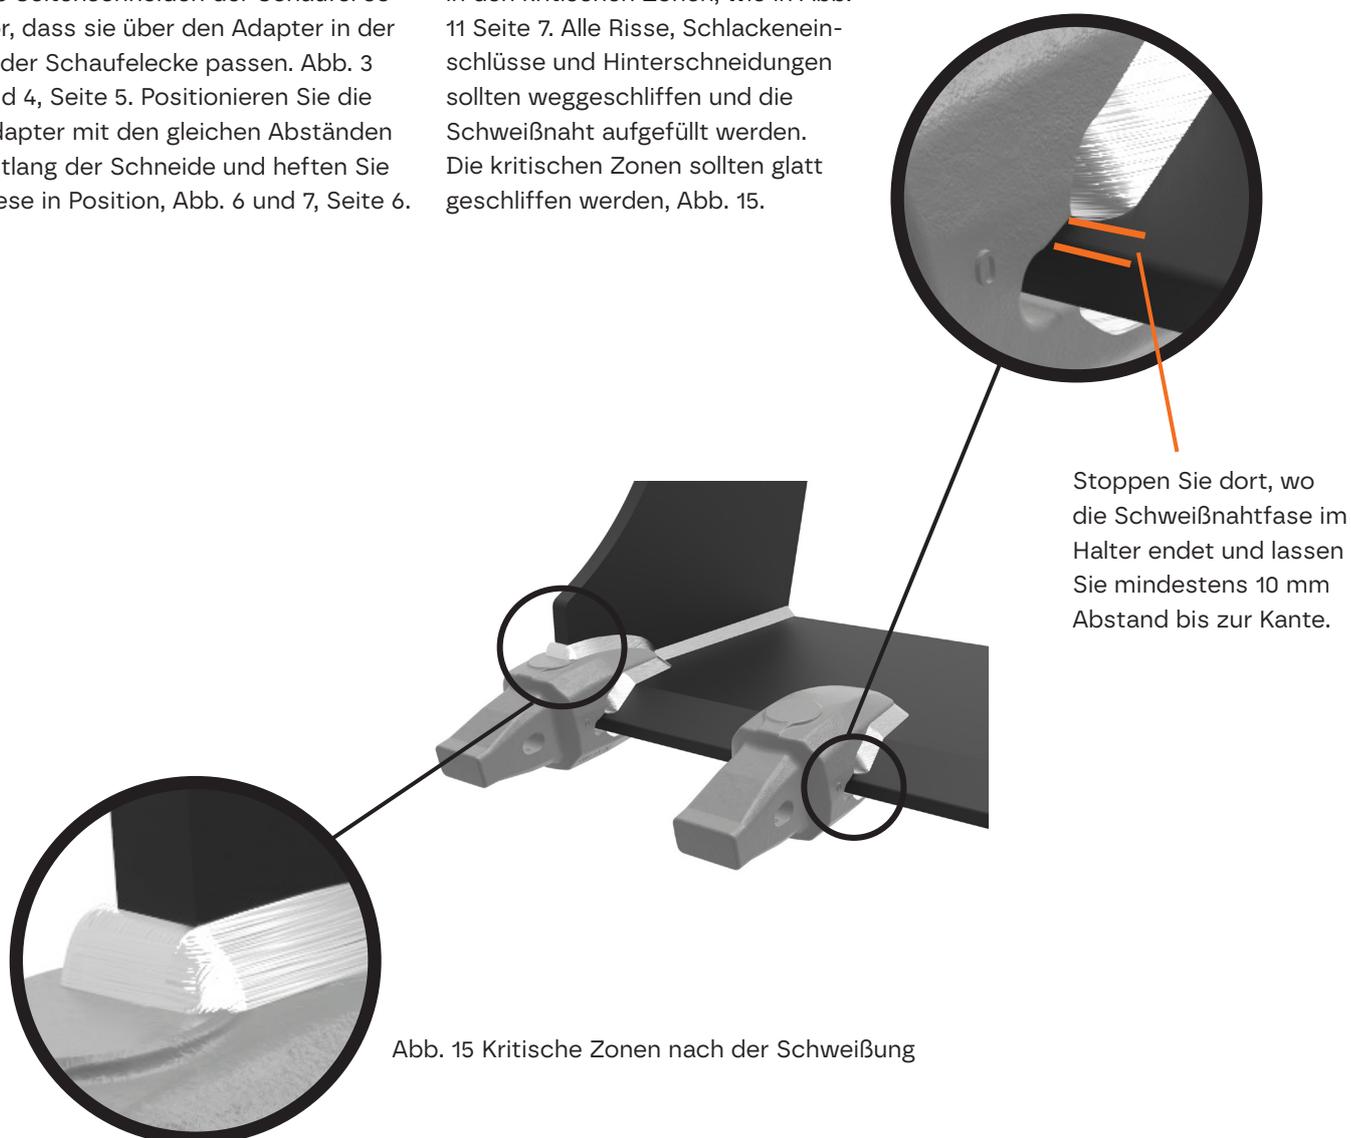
Kritische Zonen nach der Schweißung
